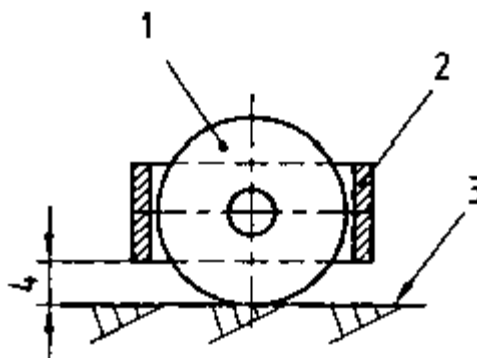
Защитный кожух колеса: 1 - колесо; 2 - кожух колеса; 3 - пол; 4 - промежуток (не более 35 мм)
